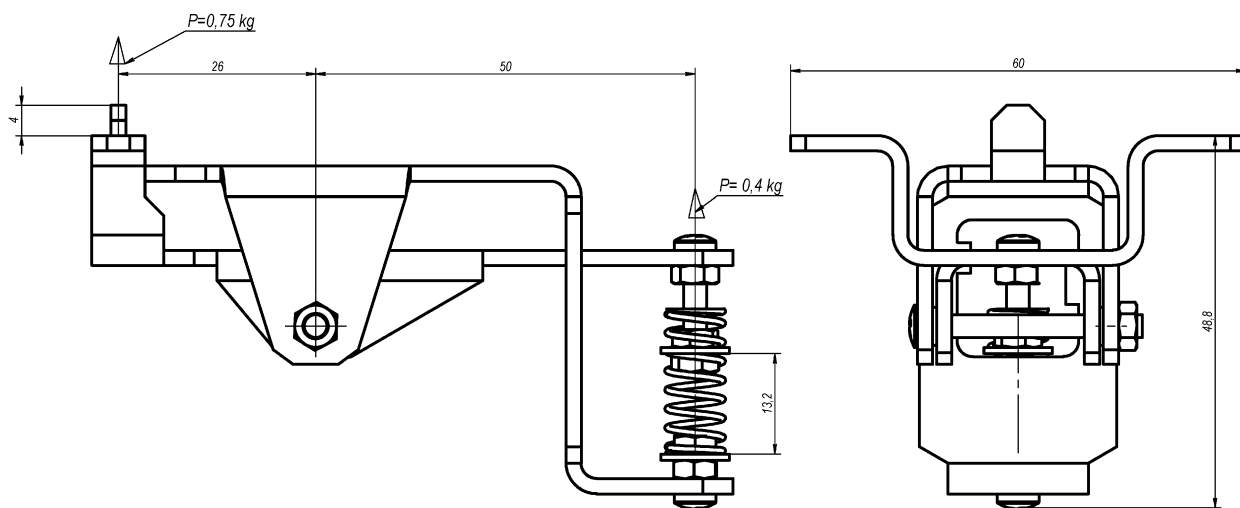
Приспособление для регулировки натяжения ремня EBKM.00D800.П2.00.000
